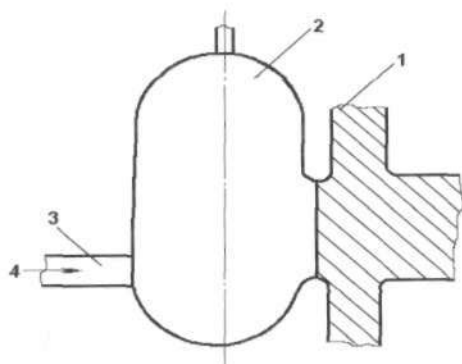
Боковая прибыль для отливки из ковкого чугуна:
